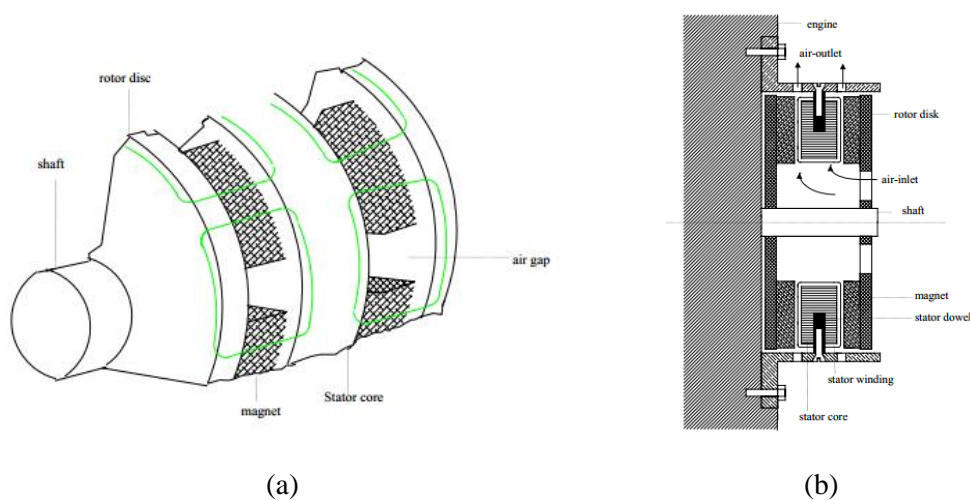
TORUS à bobinage toroïdal : (a) représentation de la machine et (b) section de la machine [34].
